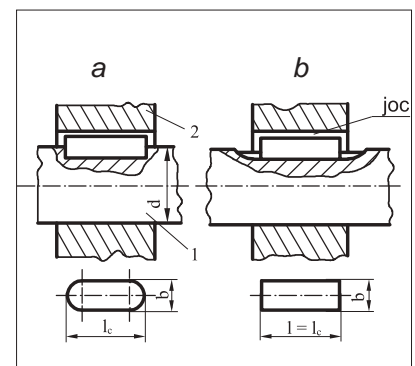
Reprezentarea asamblărilor prin pene paralele: a – pană paralelă cu capete rotunde; b – pană paralelă cu capete drepte
